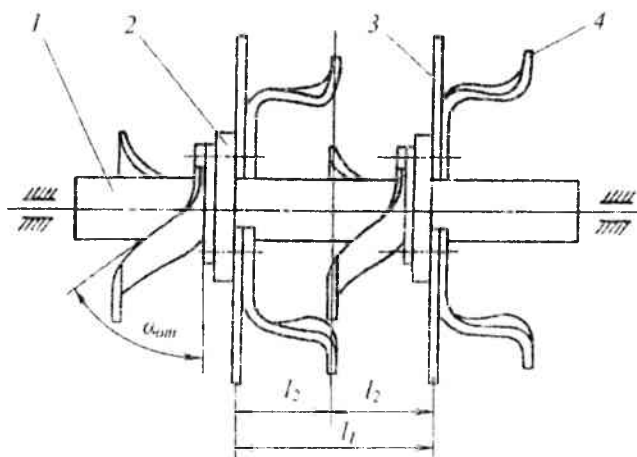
Ротационный рабочий орган с усовершенствованными составными ножами для послойной обработки почвы: 1 – вал ротора; 2 – диски; 3 – основной прямой нож; 4 – дополнительный боковой Z-образный нож
